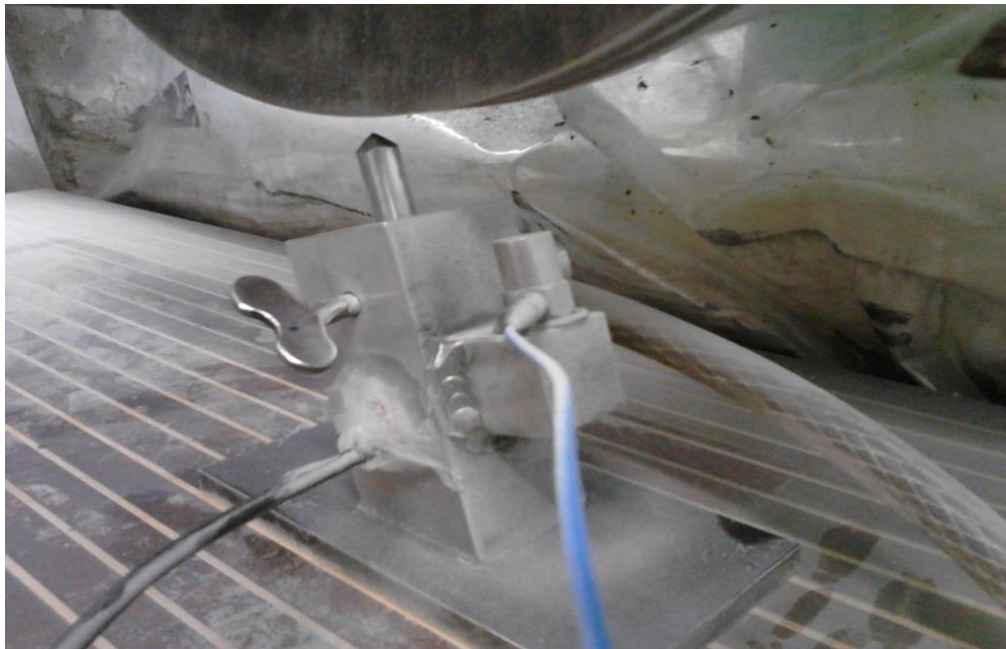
Montagem do dressador, com o dressador, suporte do dressador e dos equipamentos de medição conectados a ele.
